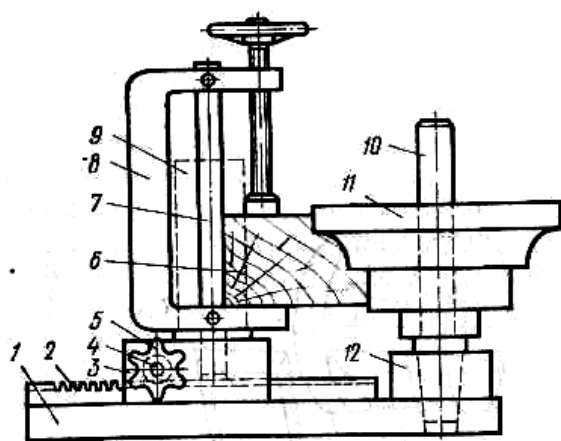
Контрольно-установочное приспособление для настройки сборных фрез:
